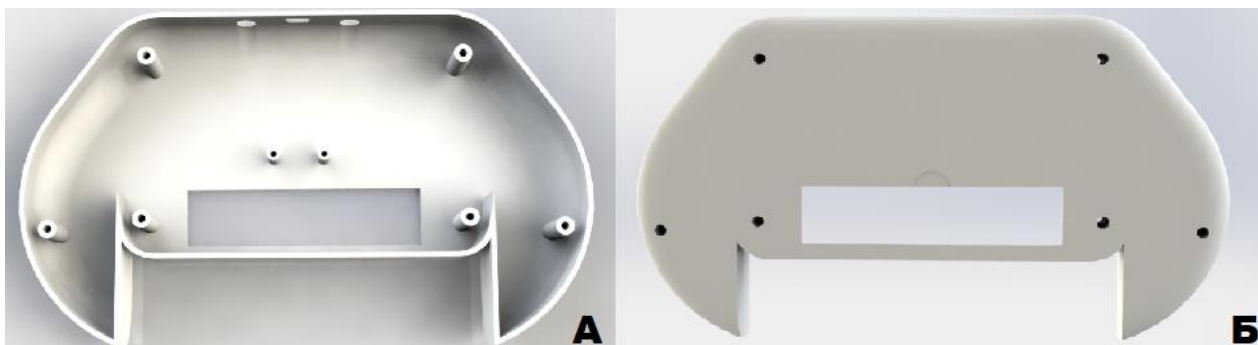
Нижня частина аналізатору: А – вид зверху, Б – вид знизу
